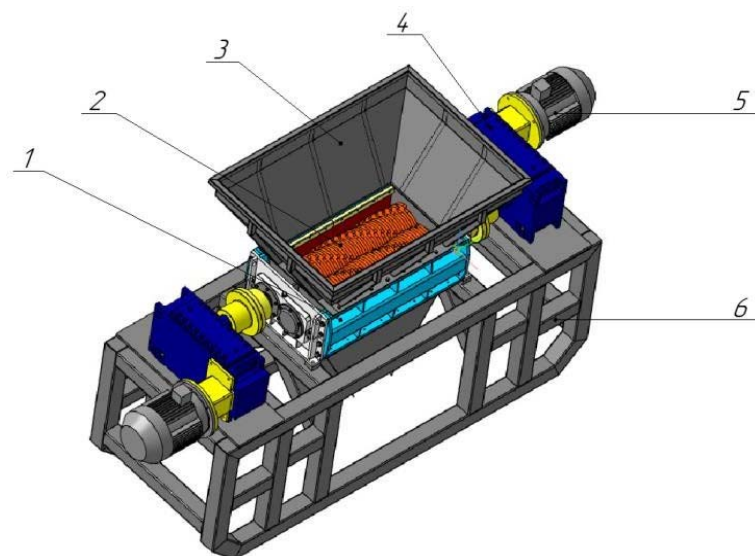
Двухроторный шредер: 1 – блок измельчения; 2 – ротор с режущими ножами; 3 – загрузочное окно; 4 – редуктор; 5 – электродвигатель; 6 – рама
